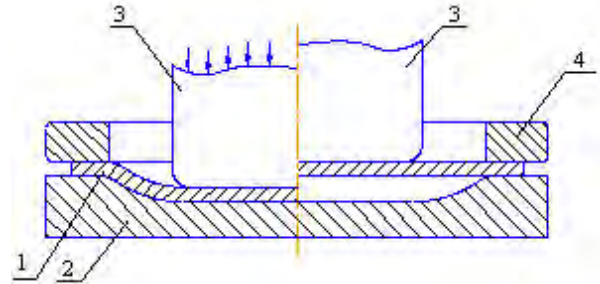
Схема формовки рифта укороченным пуансоном: 1 – заготовка; 2 – матрица; 3 – пуансон; 4 – прижим
